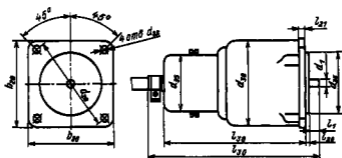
Габаритные и установочные размеры двигателя МТС-200-8
